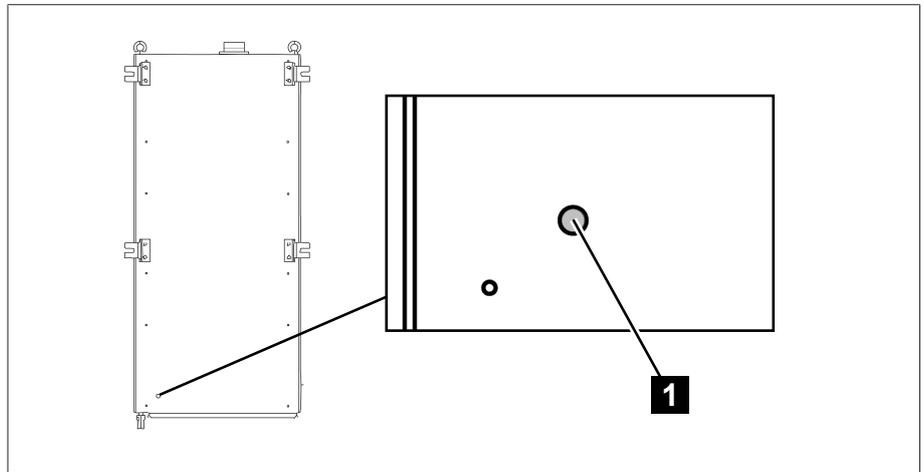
Elemento di compensazione della pressione sul retro dell'apparecchio
